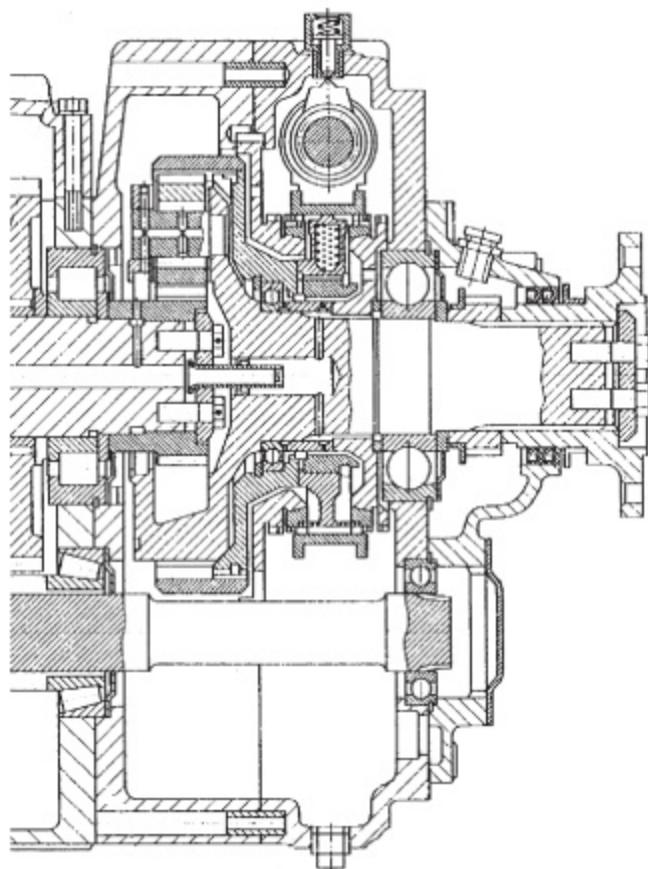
Конструкция дополнительного планетарного редуктора коробки передач грузового автомобиля
